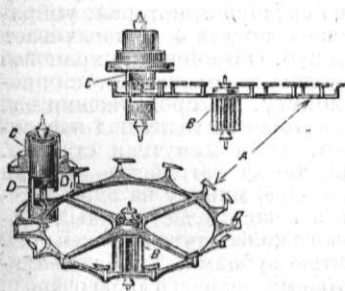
Цилиндрический ход. А — цилиндрическое колесо, В — триб цилиндрич. колеса, С — цилиндр, D — входная губа, D₁ — выходная губа.
